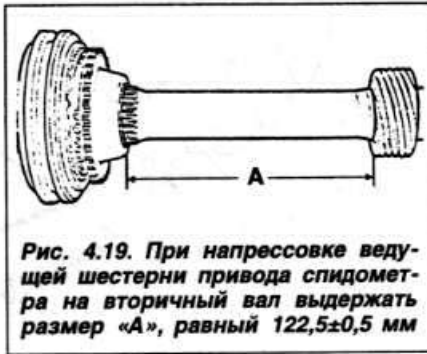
При напрессовке ведущей шестерни привода спидометра на вторичный вал выдержать размер «А», равный $122,5 \pm 0,5$ мм
